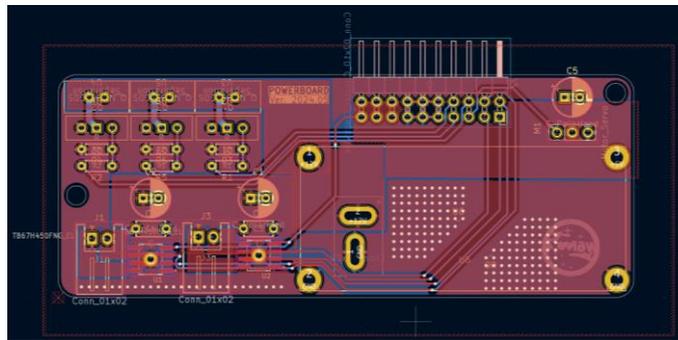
回路の配線並びに配置図 (モータ系統)
